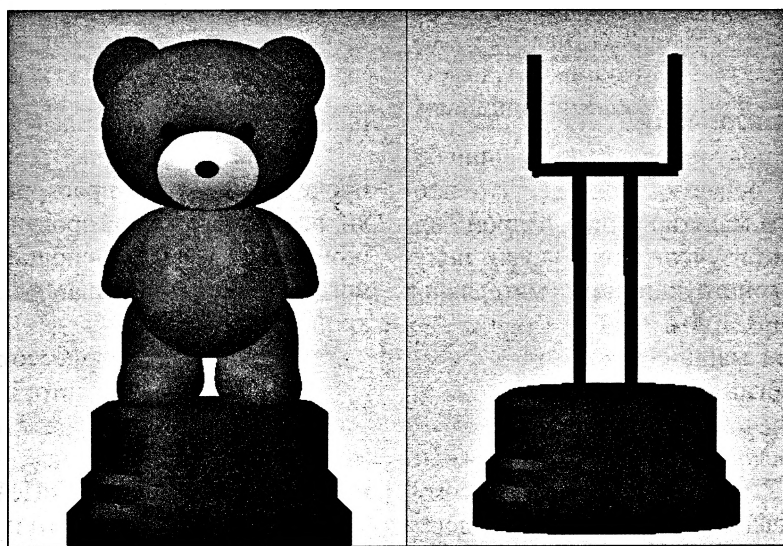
3D-модель в сборе и подставка с каркасом для сборки изделия
